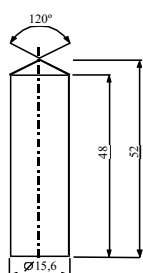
Pistón cilíndrico de bronce, dimensiones en mm.
